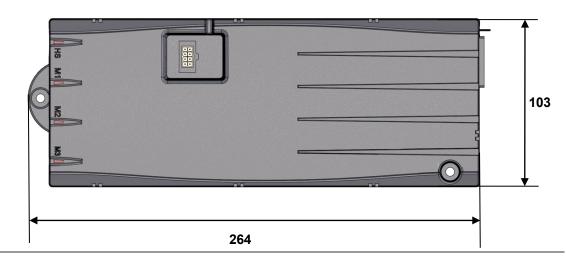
Steuerung COMPACT, Draufsicht (Angaben in mm)
